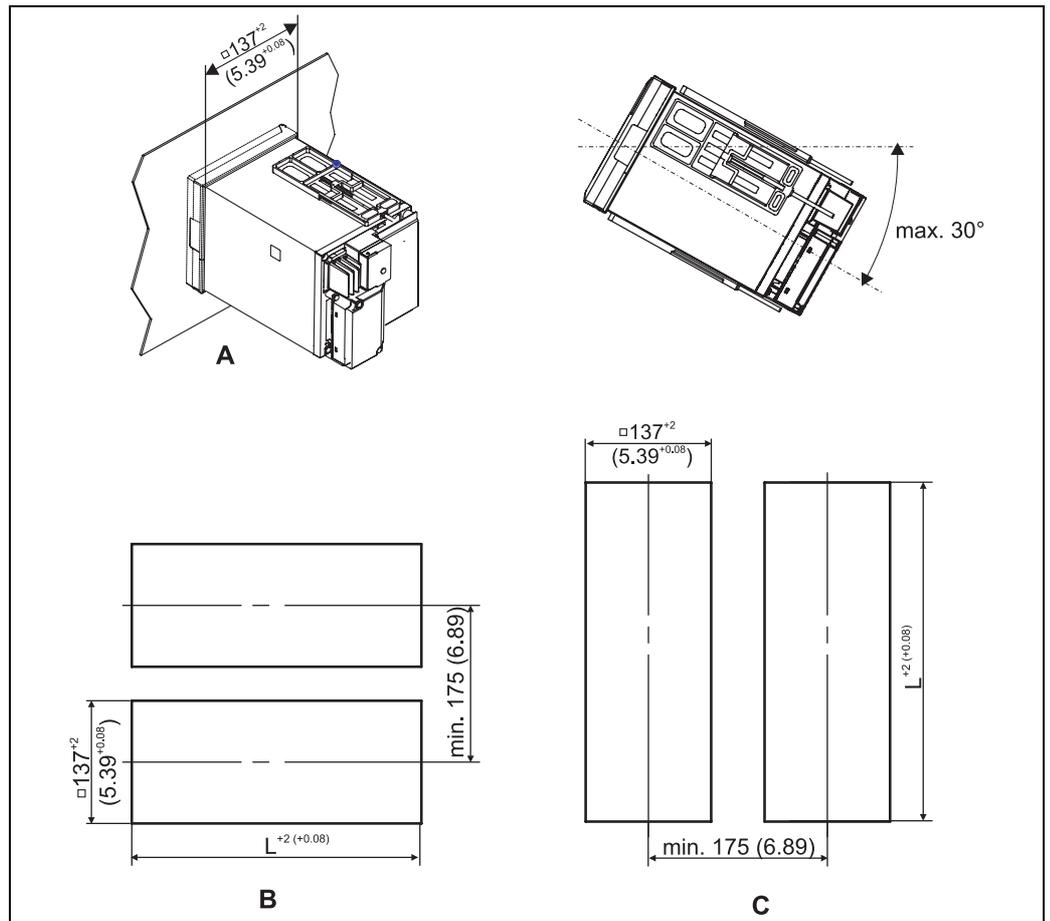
Schalttafelausschnitt - Abmessungen in mm (inch)
